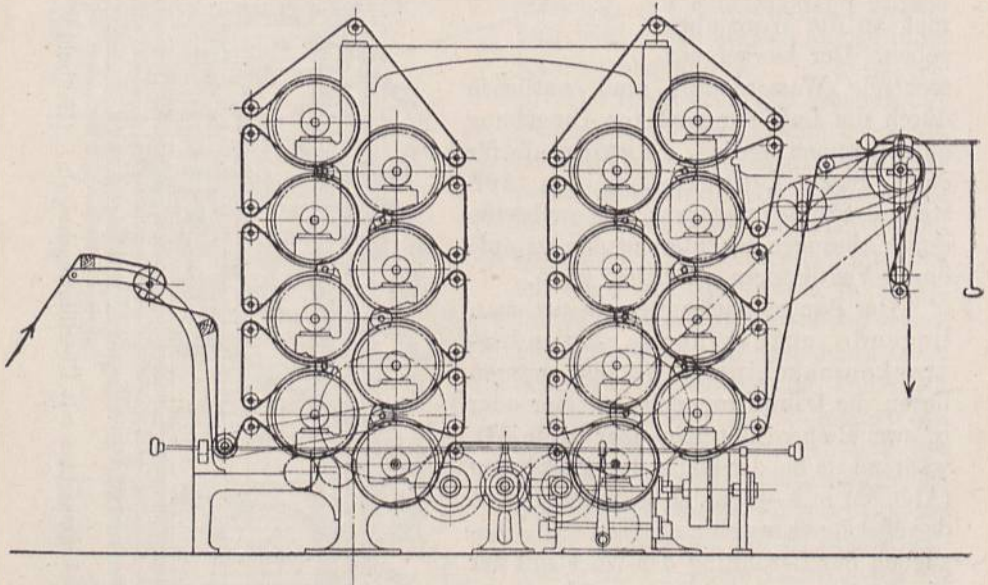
Stehende Zylindertrockenmaschine. (Haubold.)
